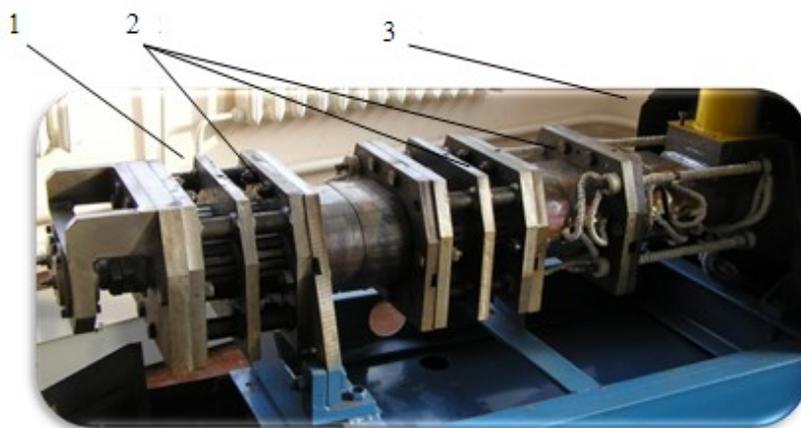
Зовнішній вигляд корпусу екструдера ЕК 75/1200:
